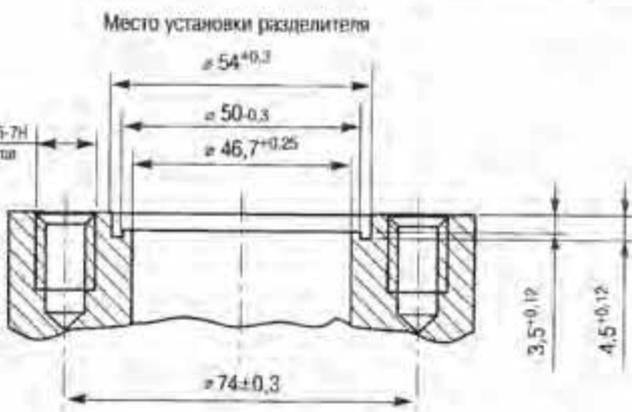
Габаритные и присоединительные размеры разделителя мембранного РМ модели 5322
